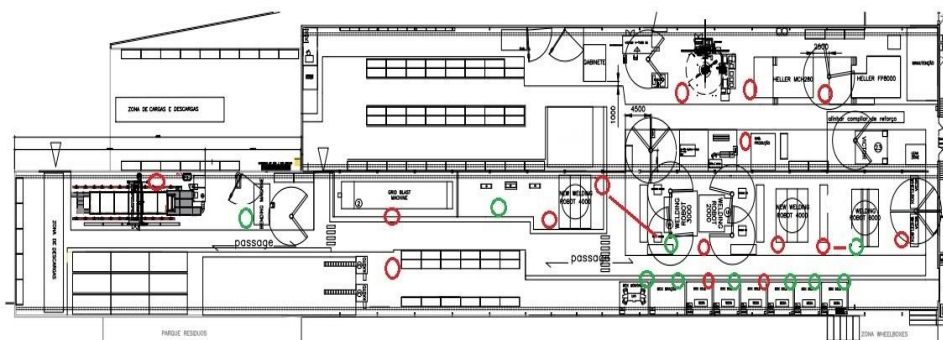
Planta do chão de fábrica com terminais de picagem.
